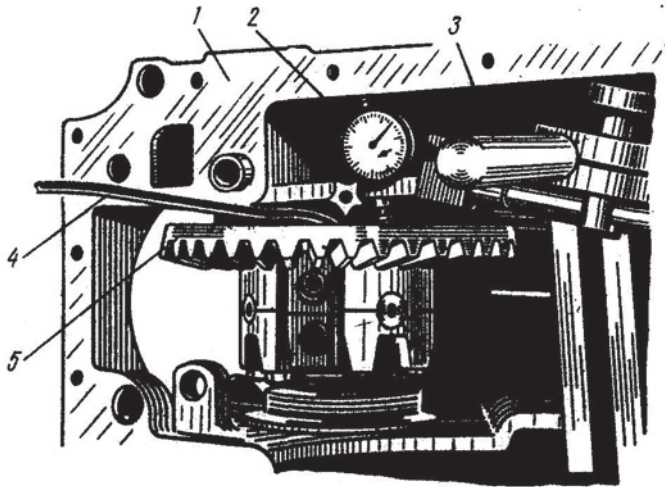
Проверка осевого зазора в роликоподшипниках.
